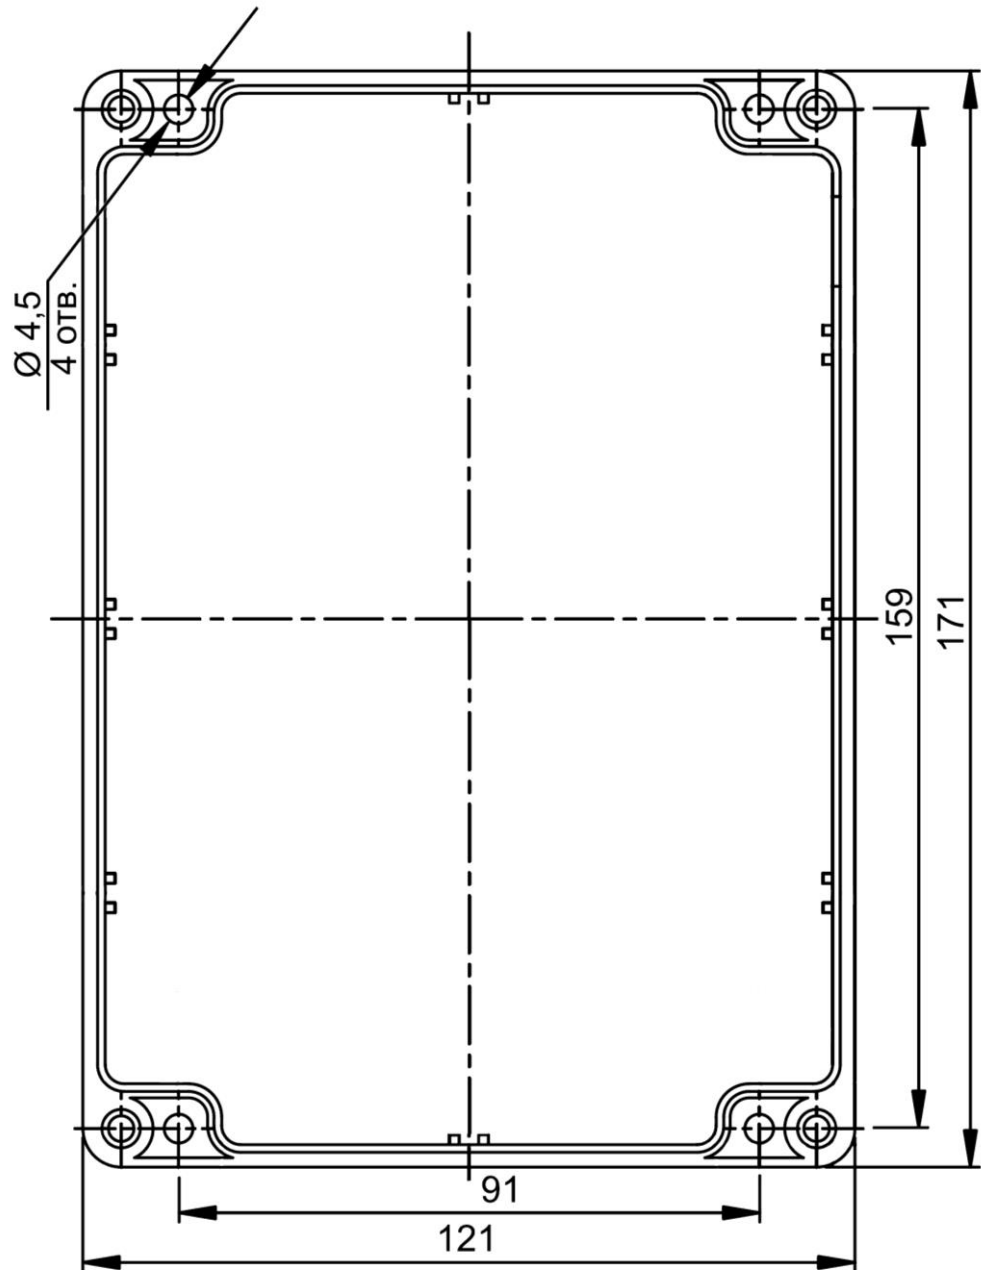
Размеры монтажного бокса и расположение крепежных отверстий
